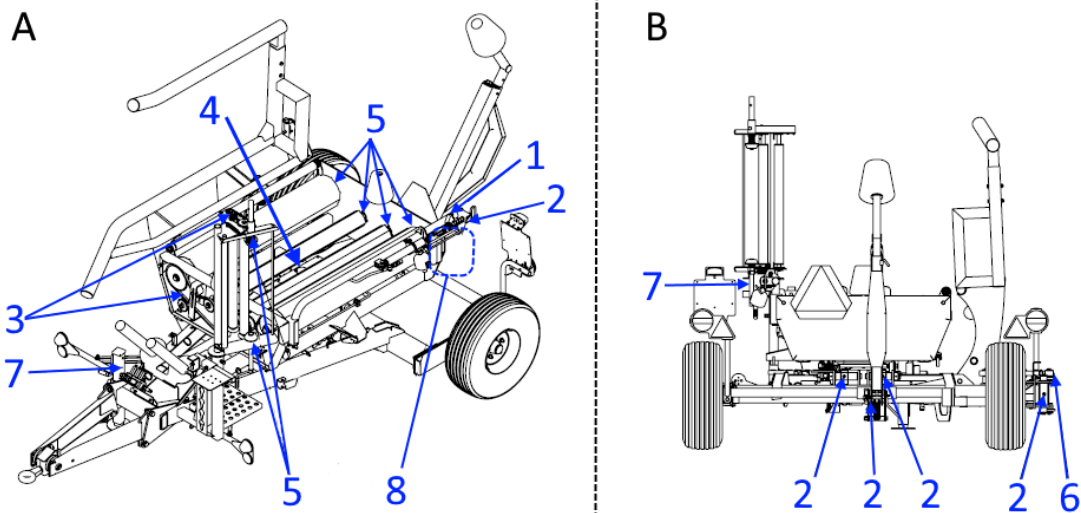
Points de graissage : A – vue diagonale, B – vue arrière
